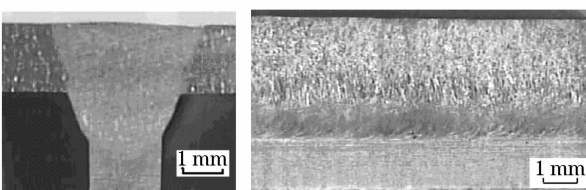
T 型接头复合焊接的焊缝横、纵截面
